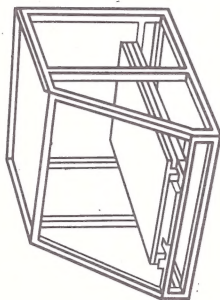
Стеллаж для приспособлений с выдвинутой платформой СД3725.01А
